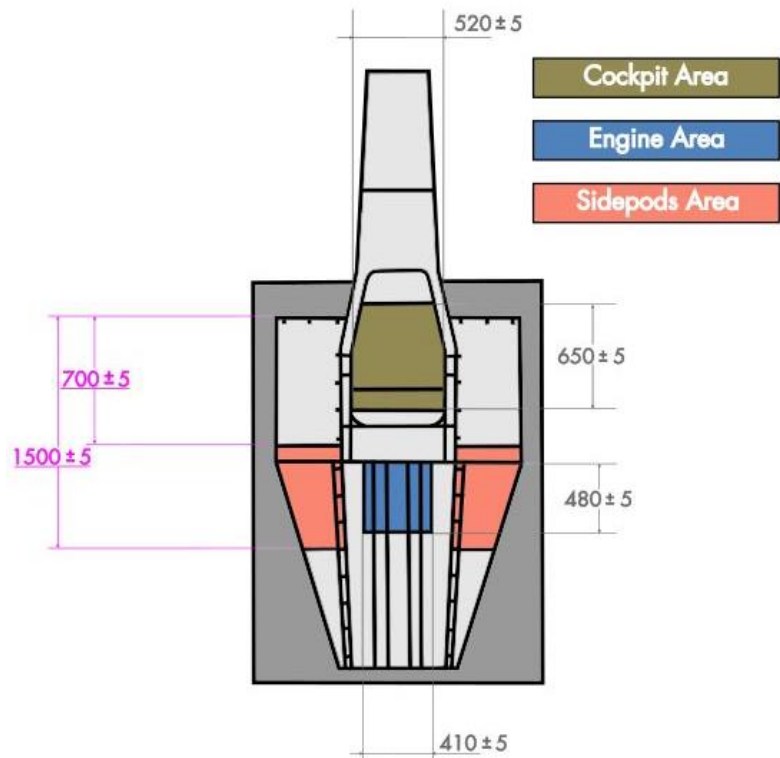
Emplacement des assemblages de combustion sur le banc d'essai d'incendie
